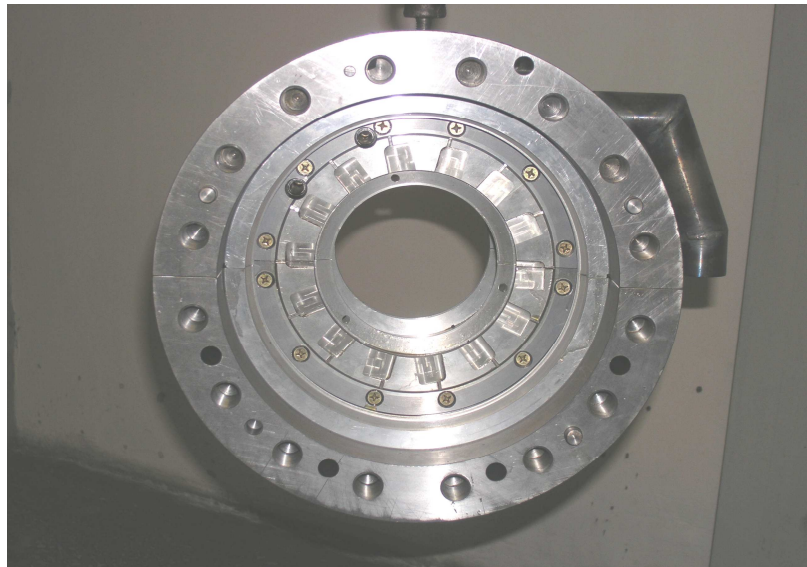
Общий вид подшипника опорно-упорного ПДУ-120-Т3 турбины 103JT
